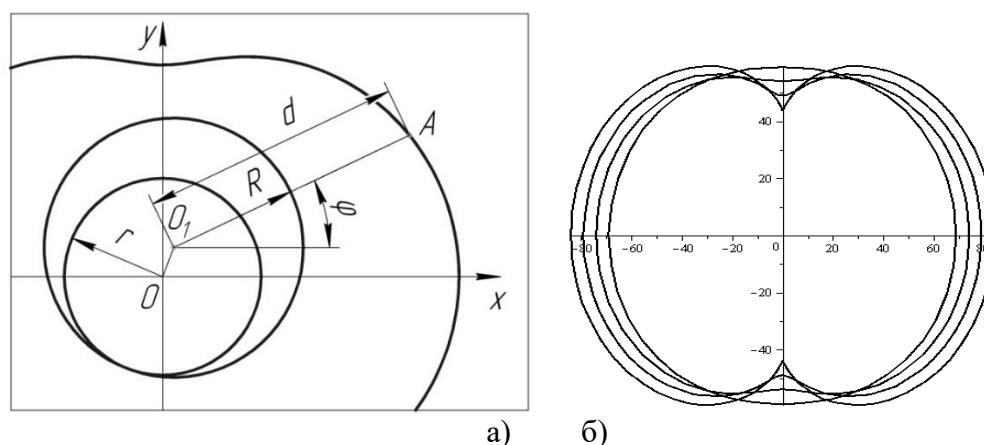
Формування профілю корпусу компресора: а – схема утворення
